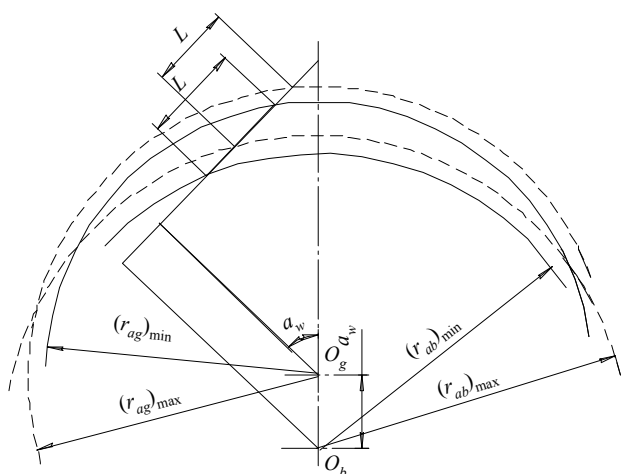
Схема зацепления колес передачи типа К-Н-V
